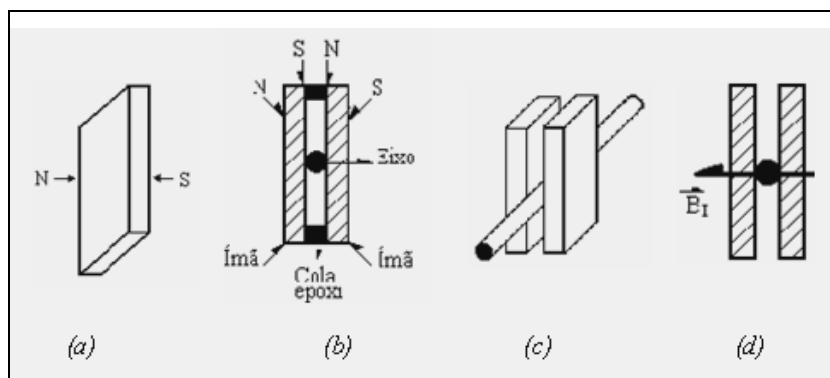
(a) o ímã facial; (b) a montagem do rotor (observe a polaridade de cada face); (c) o rotor montado e (d) o vetor campo magnético \vec{B}_1 , que passa pelo eixo do rotor.
